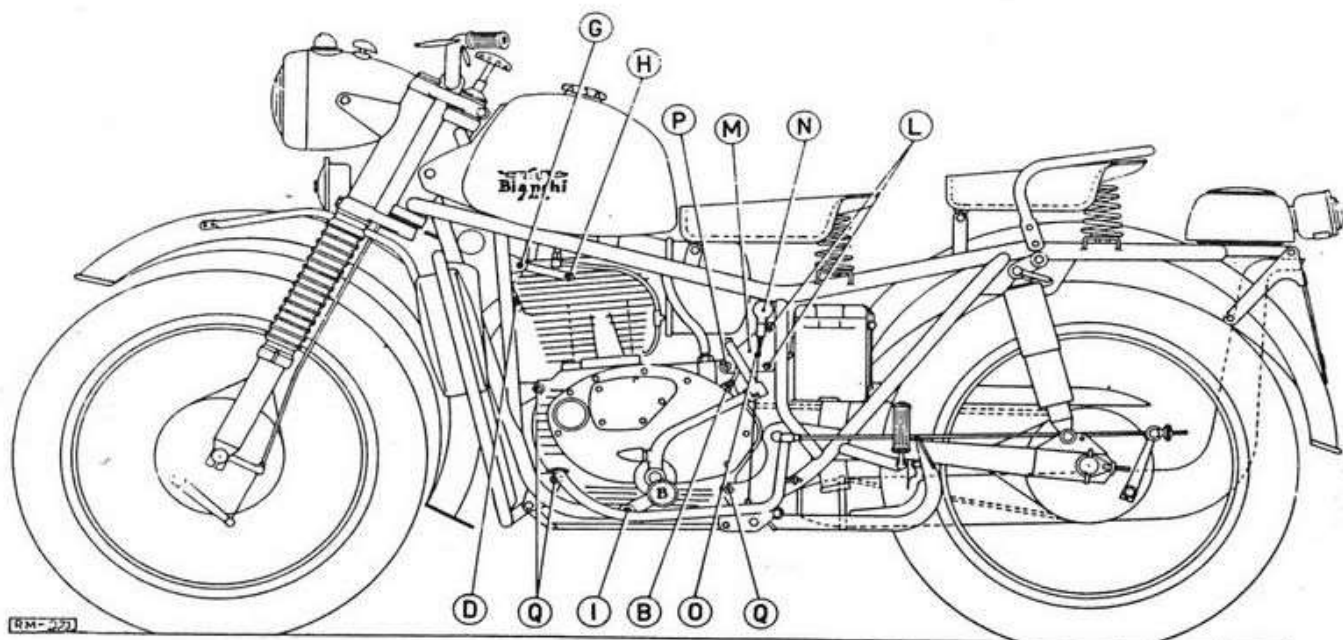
Rimozione del motore del veicolo: parti da smontare sul lato sinistro.
